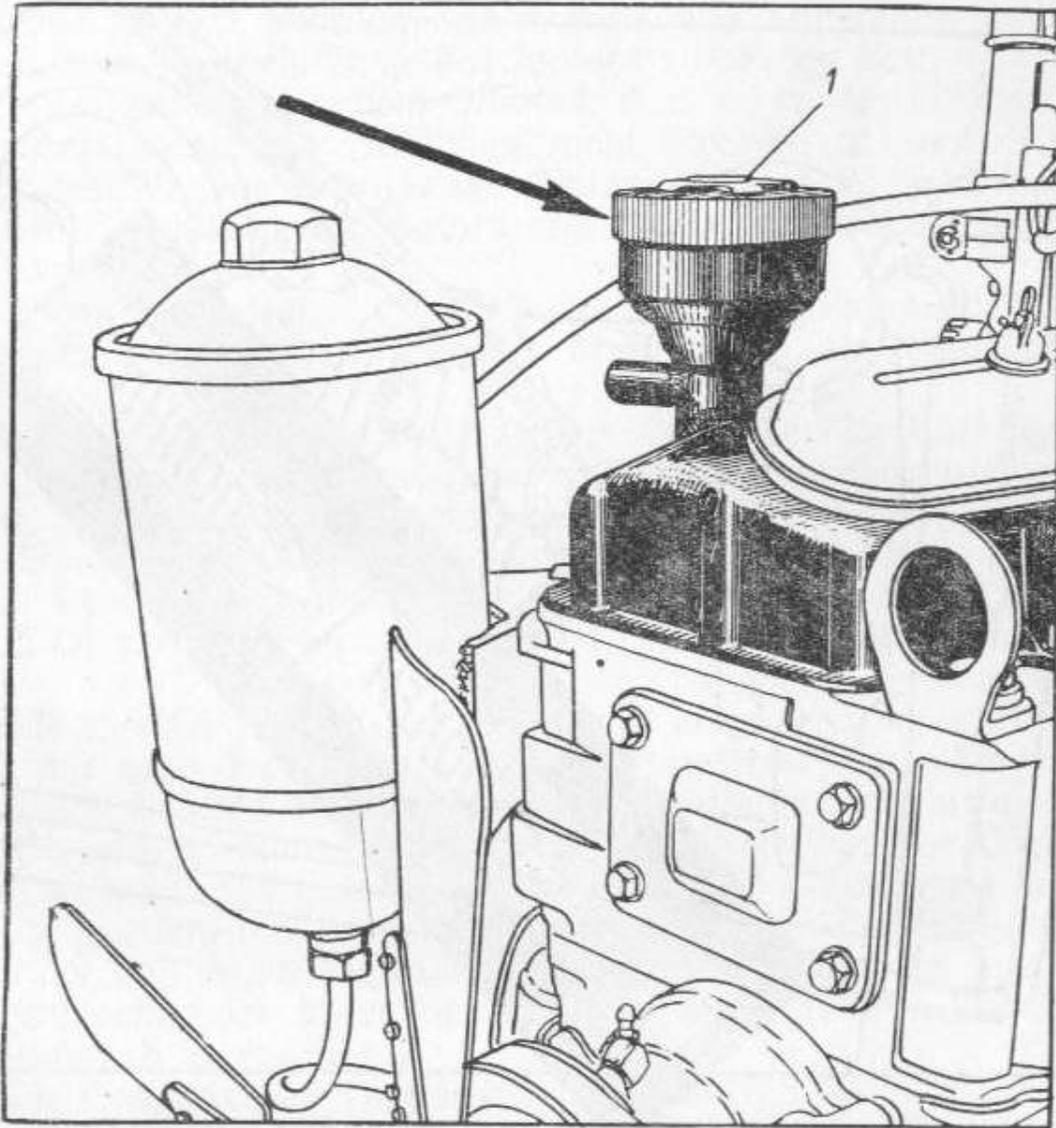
Öleinfüllstutzen am Kurbelgehäuse des Motors
